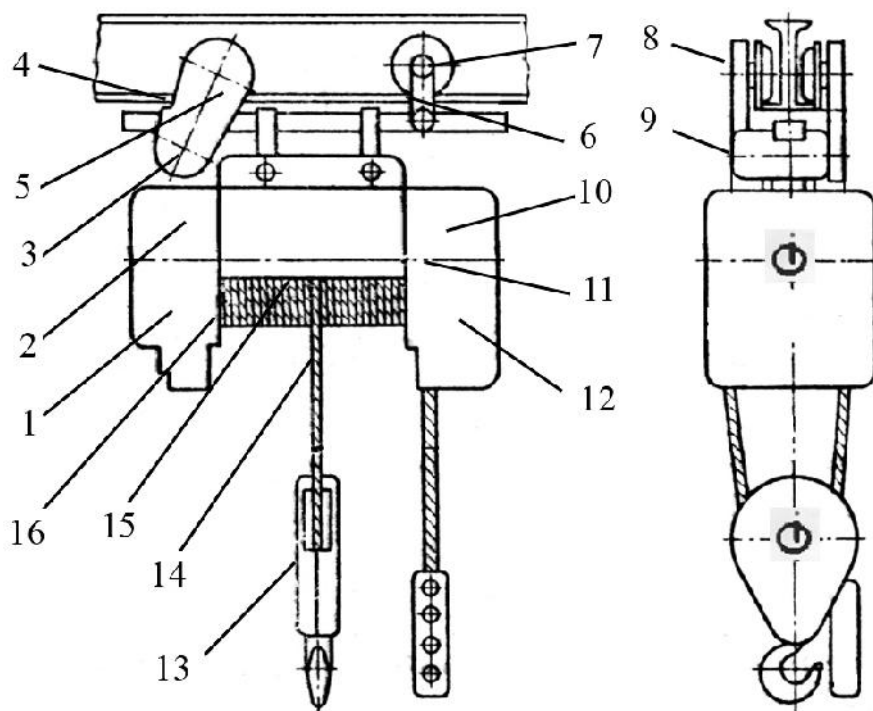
Схема смазки типовой тали: 1 – редуктор механизма подъема; 2 – шарниры колодочного тормоза; 3 – правый редуктор приводной тележки механизма передвижения; 4 – направляющие ролики тележек механизма передвижения; 5 – шарнир поворота приводной тележки механизма передвижения; 6 – шарнир поворота не приводной тележки; 7 – подшипники катков не приводной тележки; 8 – левый редуктор приводной тележки механизма передвижения; 9 – подшипник вала электродвигателя приводной тележки; 10 – шарниры шкафа электроаппаратуры; 11 – подшипник вала электродвигателя механизма подъема и барабана; 12 – шарниры ограничителя подъема и спуска; 13 – подшипники крюка и блока подвески; 14 – грузовой канат и поверхность барабана; 15 – отбортовка сварного корпуса у талей с канатоукладчиком; 16 – зубчатая муфта и подшипник электродвигателя подъема
